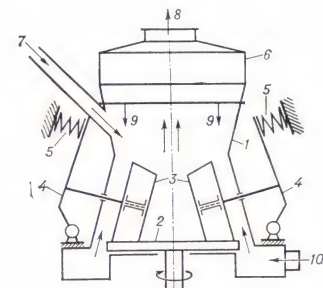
Роликовая среднеходная мельница: 1 — корпус; 2 — мелющее кольцо; 3 — ролик; 4 — нажимной рычаг; 5 — нажимная пружина; 6 — воздушный классификатор; 7 — подача измельчаемого материала; 8 — измельчённый продукт; 9 — крупный продукт классификатора; 10 — подача воздуха.
